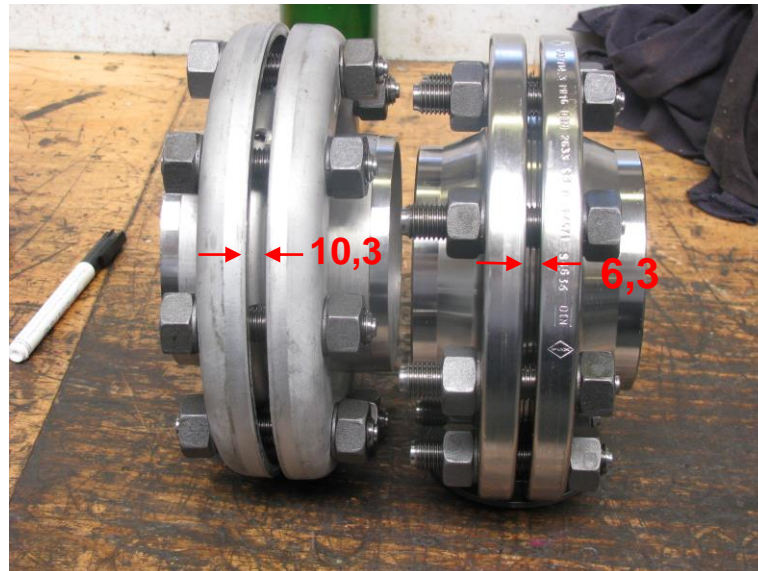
Flanschverbindungen vor Aufbringung der Schraubenkräfte
